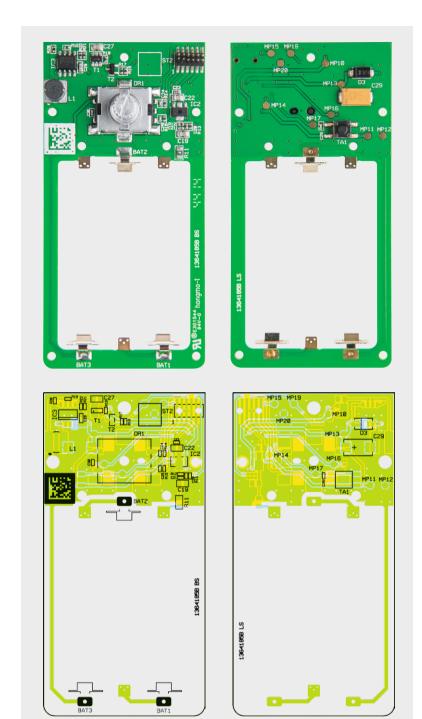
Platinenfoto der bestückten Encoderplatine mit zugehörigem Bestückungsplan
